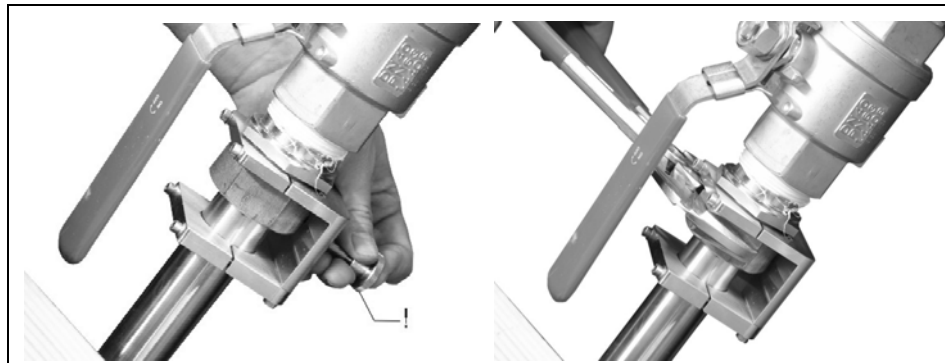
Fixieren der Überwurfmutter mittels Rändelschraube
